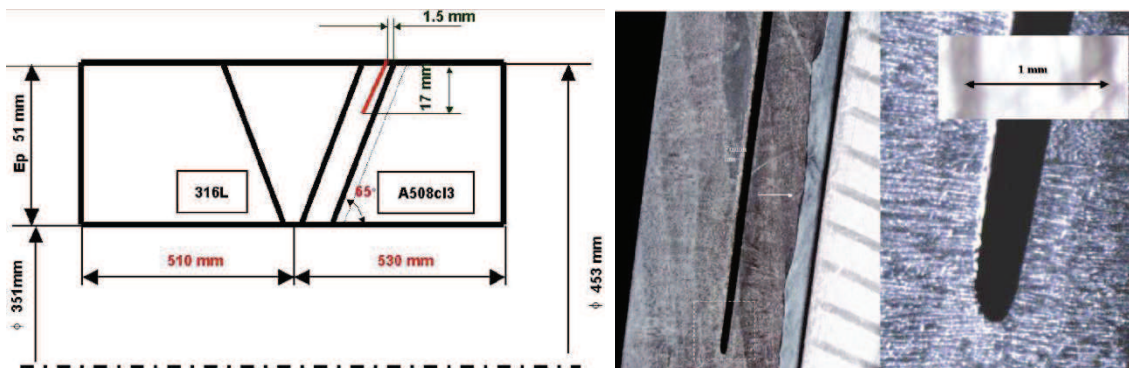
Insertion du défaut dans la soudure [FAI 08-1]
